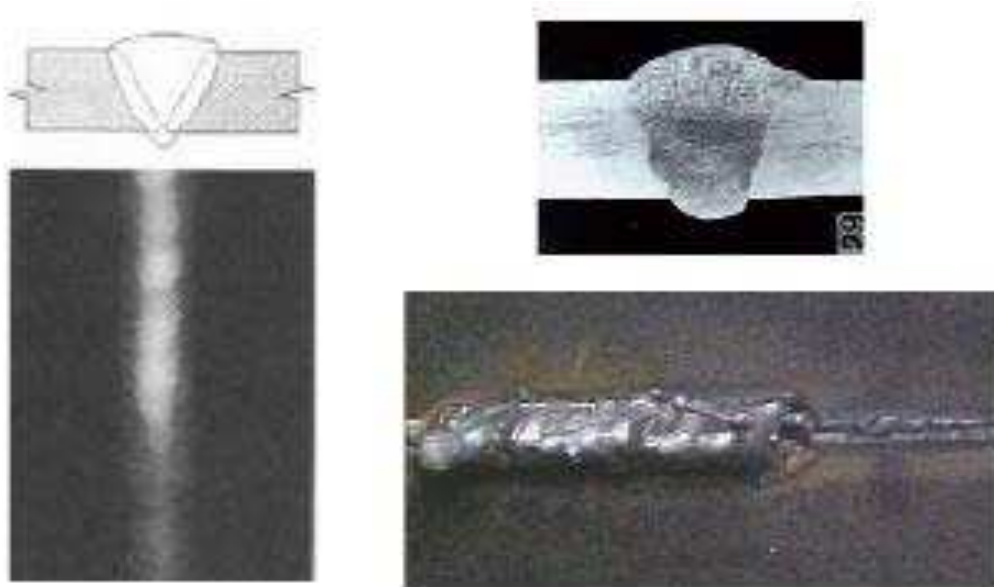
1 *Junta soldada con exceso de penetración.
